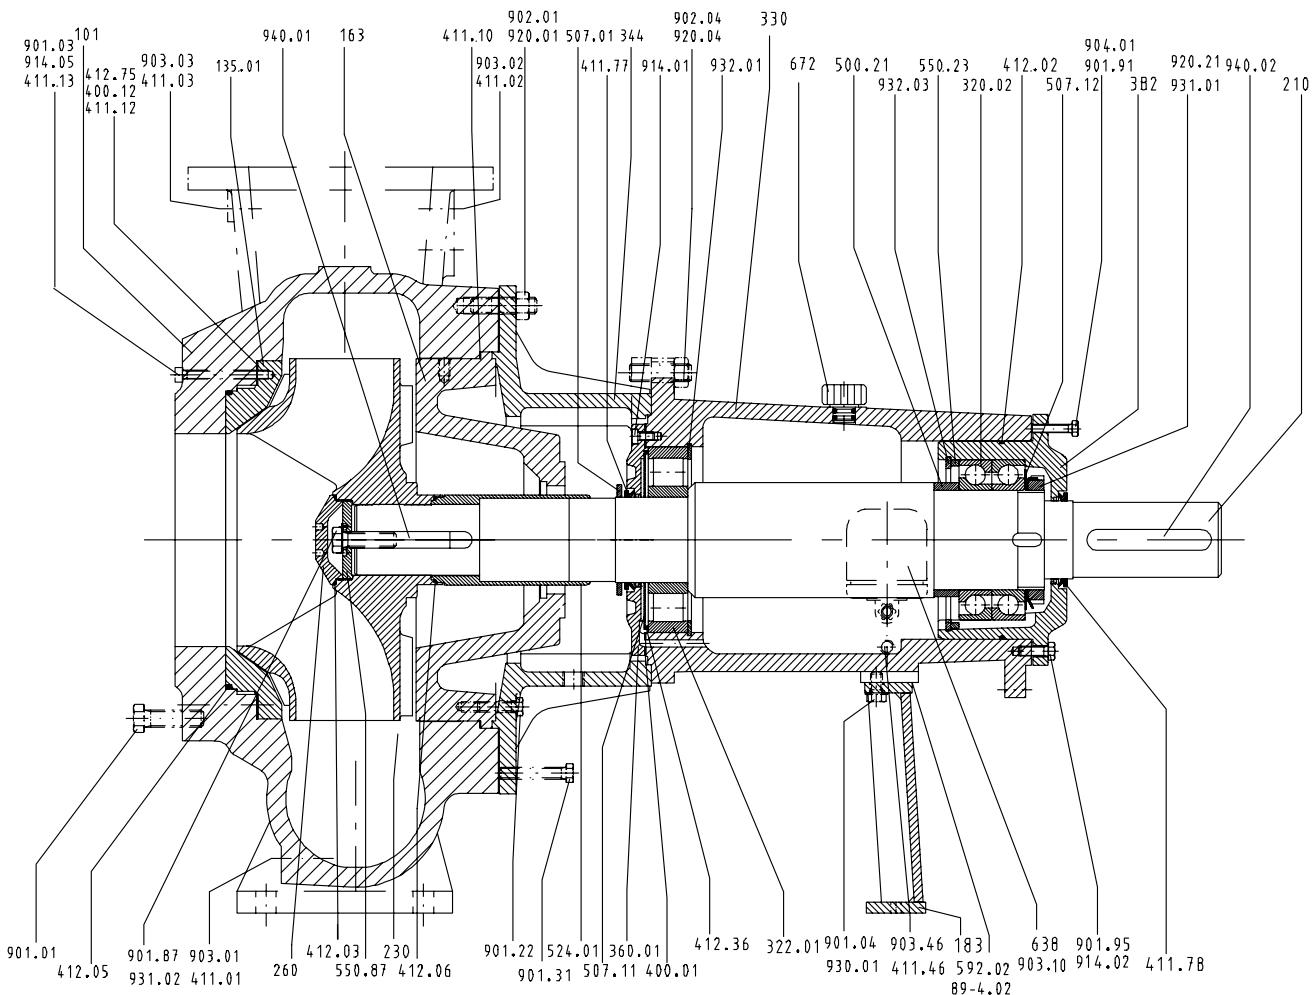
Корпуса подшипников с P08sx по P12sx
